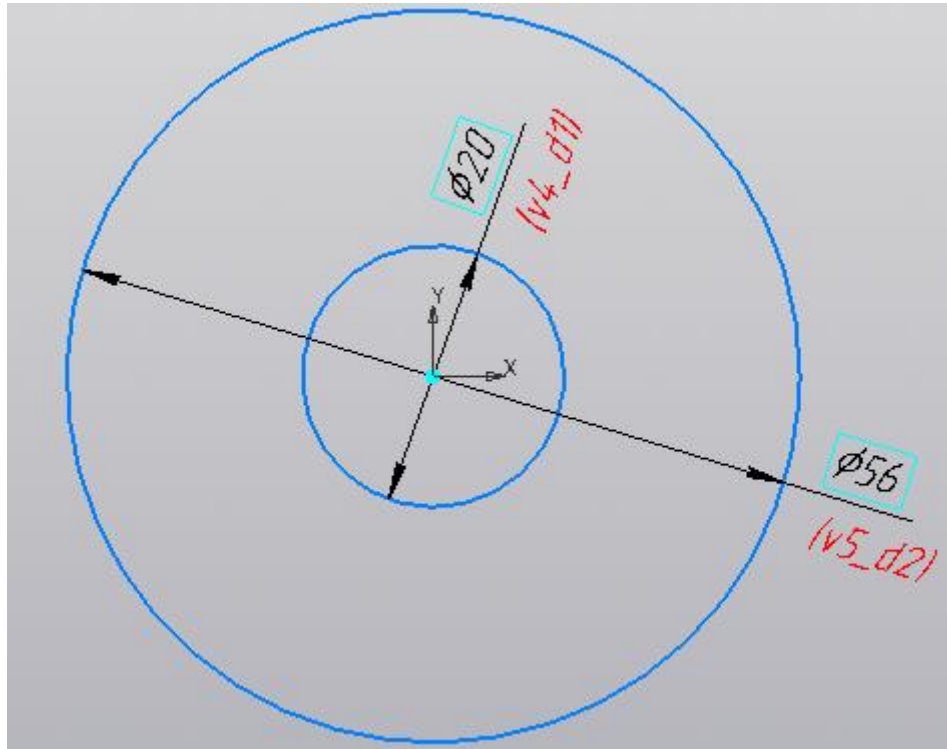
Типовой эскиз для класса изделий типа «Шайба»
